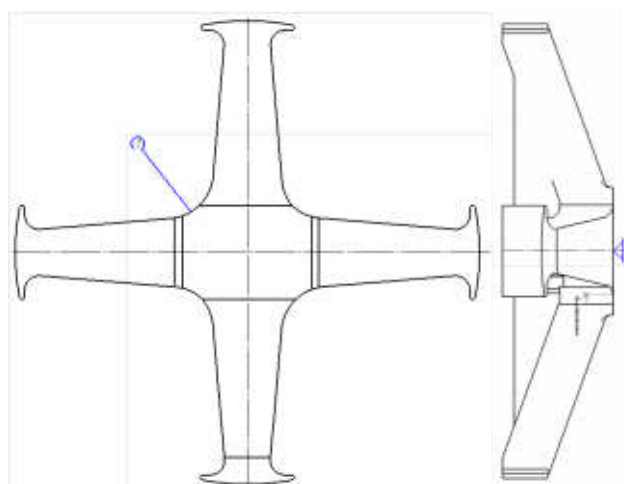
Корпус расширителя с поверхностью для захвата
